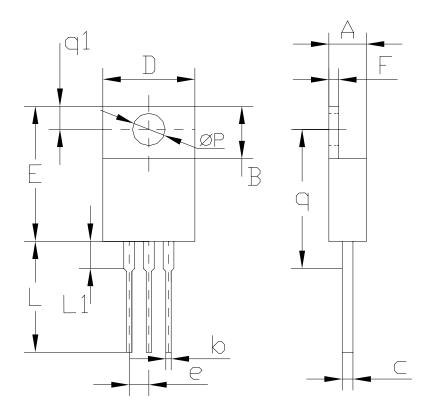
Габаритный чертеж корпуса КТ-28-2 (ТО-220АВ)
